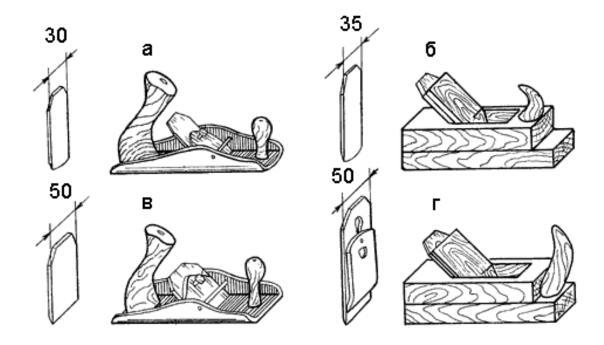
Ручные инструменты: a — шерхебель деревянный; b — шерхебель металлический; b — рубанок деревянный; c — рубанок металлический
